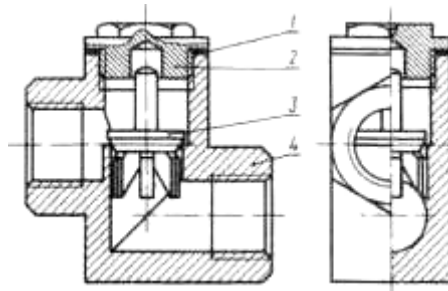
Читання креслення клапана: 1 - прокладка; 2 - кришка; 3 - клапан; 4 - корпус
